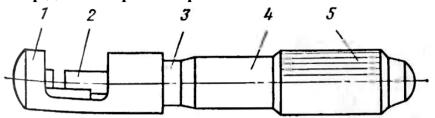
Общее устройство микрометра для измерения проволоки: 1 – корпус; 2 – микрометрический винт; 3 – стебель; 4 – барабан; 5 – трещотка
